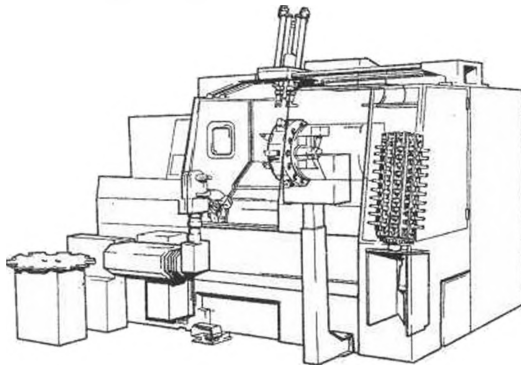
Схема токарного верстата з ЧПУ з барабанним інструментальним магазином
